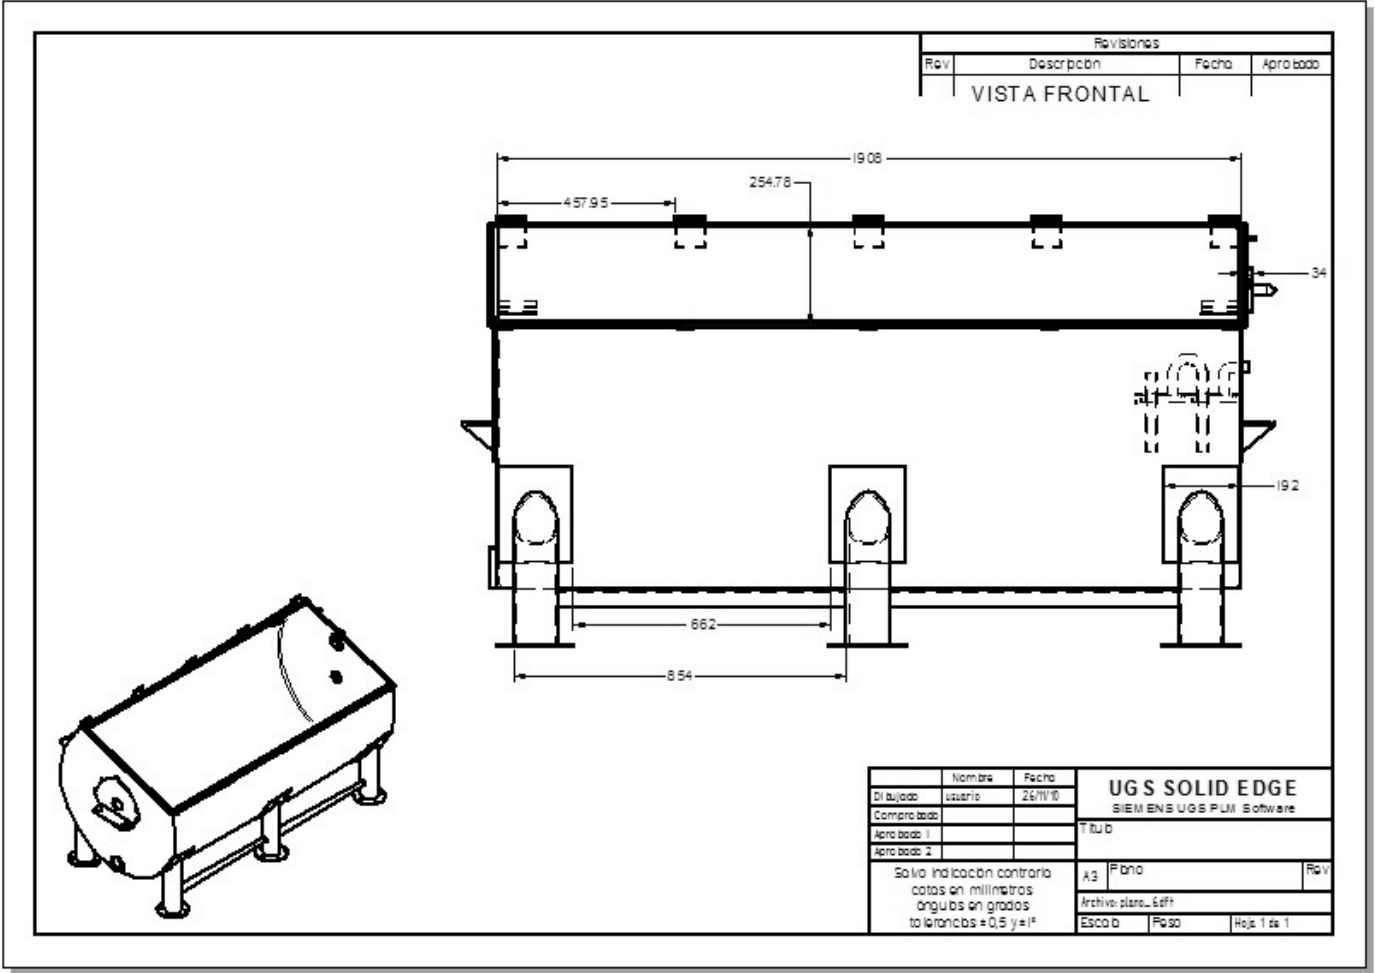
Plano del contenedor de mezclado, vista frontal, detalle 4.
